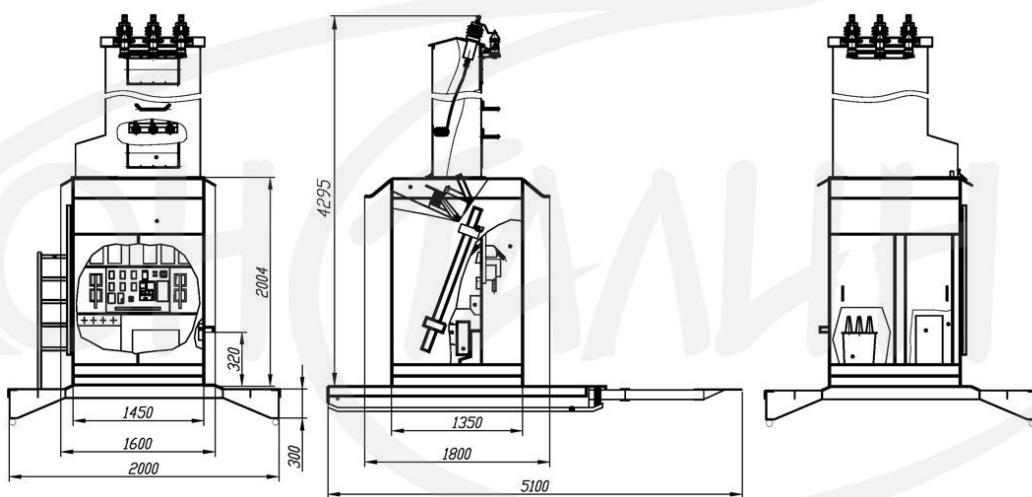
Конструктивный чертеж ячейки ЯКУ1-КН
